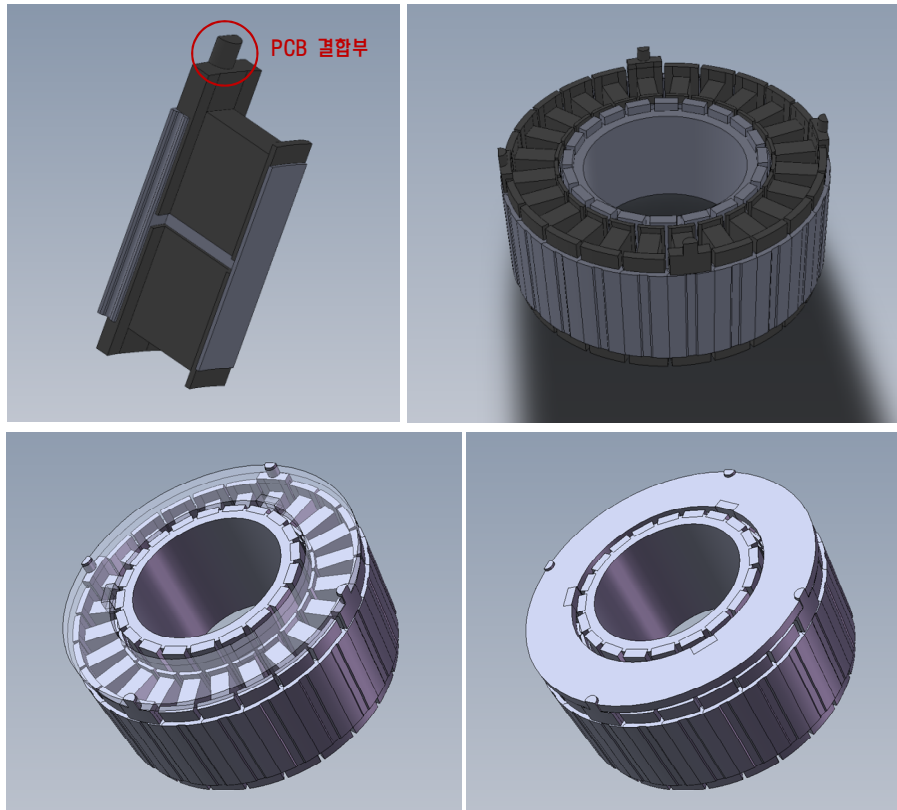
PCB 결합을 위한 돌기형 인슐레이터
